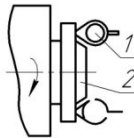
Схема проверки торцевого биения опорного буртика шпинделя передней бабки
